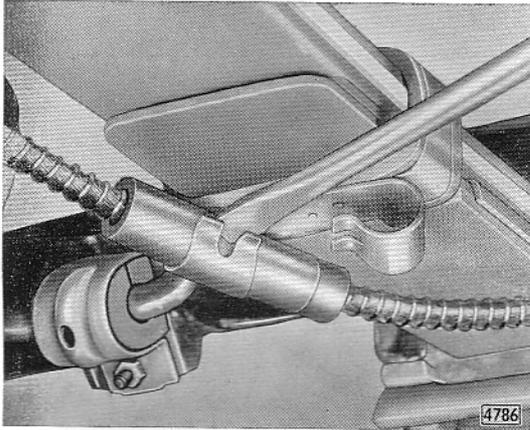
Halter an Hinterfeder für Druckschlauch des hinteren Handbremsseiles aufdrücken
